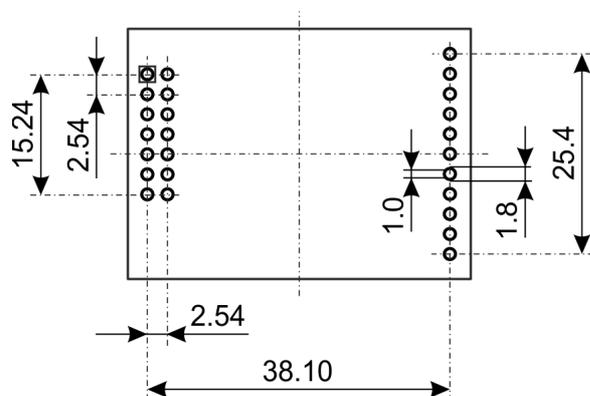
THT Footprint [mm] – Vista desde arriba
